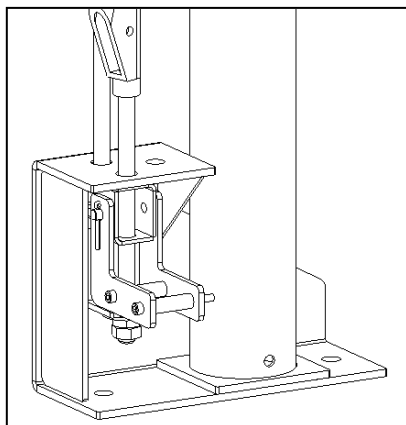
Dispositivo de teste montado no tirante inferior (posição armada para teste)
